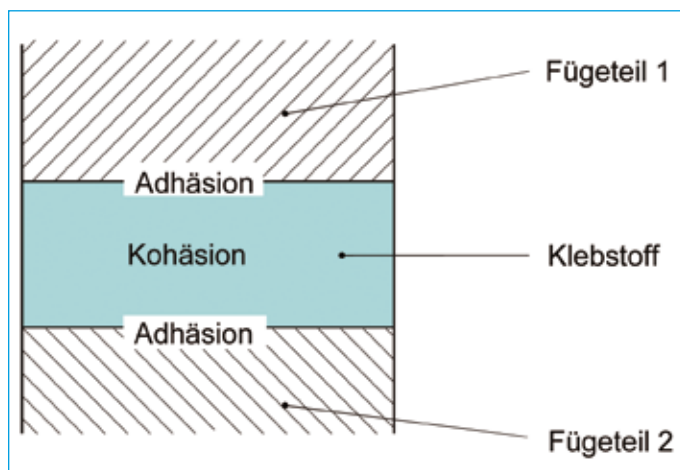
Prinzipieller Aufbau einer Klebeverbindung
